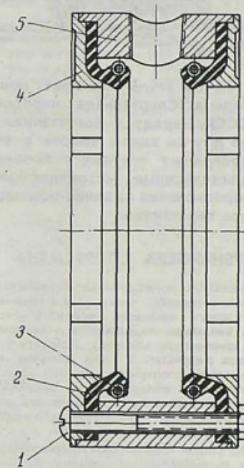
Головка подвода воздуха: 1 — винт; 2 — манжеты сальниковые; 3 — пружина манжеты; 4 — крышка; 5 — корпус.
